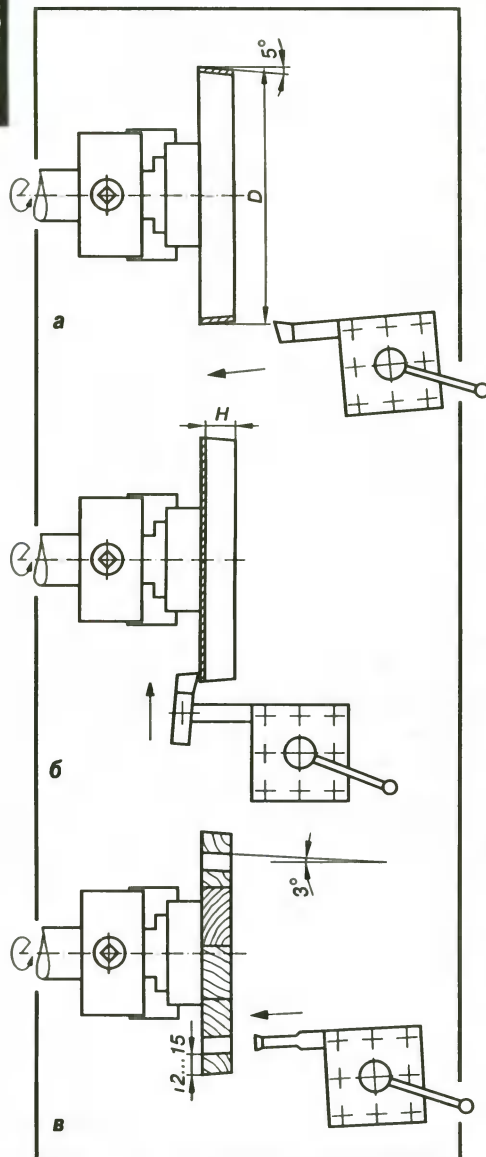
Точение колец корпуса: а — обработка по внешнему диаметру D ; б — обработка по высоте H ; в — отрезка кольца по конусу.
